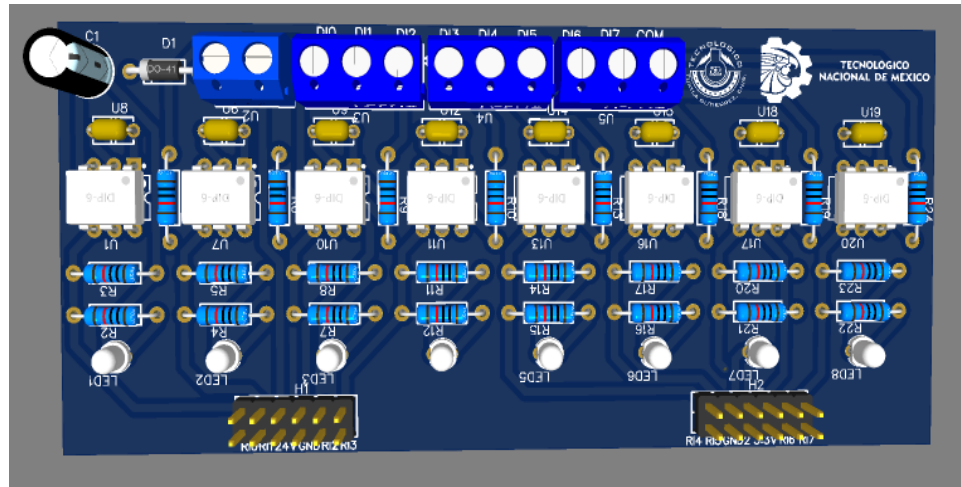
Diseño en 3D de la PCB del módulo de entrada.
